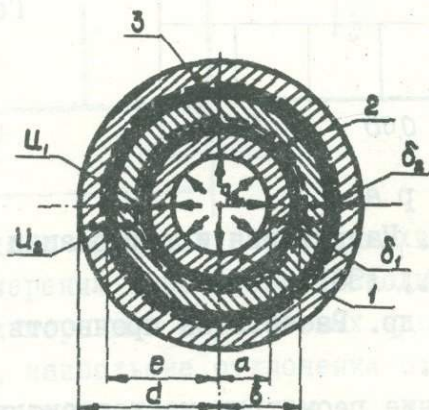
Схема нагружения зазоров и перемещений в конструкции из трех цилиндров
